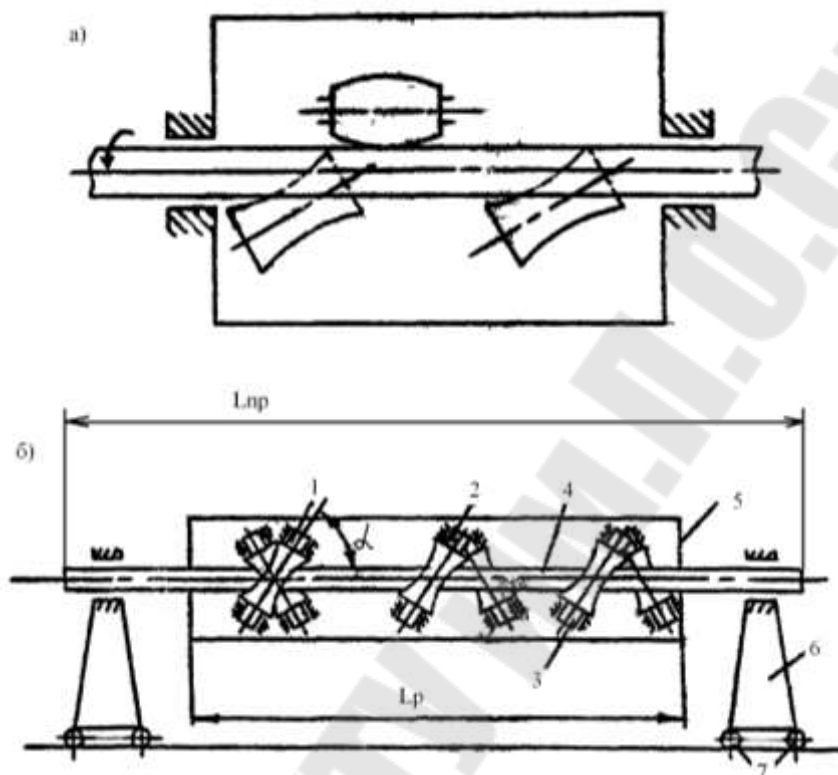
Схемы правильных станков: а) схема станка с неподвижным барабаном; б) схема станка с тремя парами роликов; 1,2,3 – пары роликов; 4 – выпрямляемый пруток; 5 – барабан; 6 – стойка; 7 – ролики
